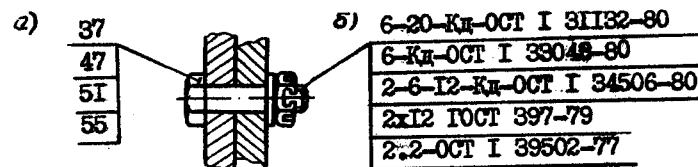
Обозначение болтового крепления на чертеже: а - по ЕСКД; б - допускается в учебном чертеже
